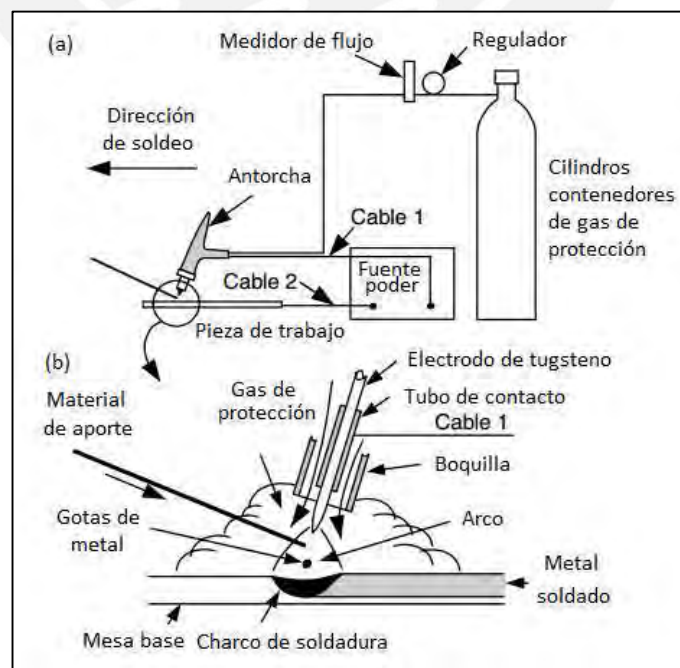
Proceso GTAW (TIG): (a) proceso general; (b) área de soldadura ampliada [11].
